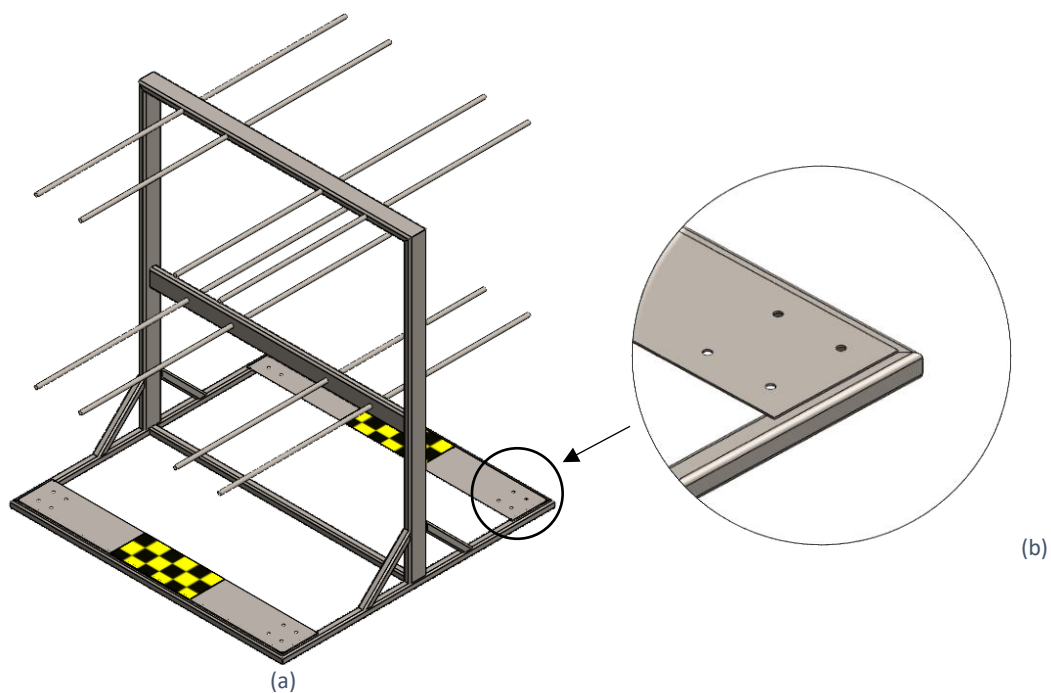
Construção da estrutura metálica: (a) montagem dos tubos para paletização e (b) detalhe dos furos para aperto das rodas.
